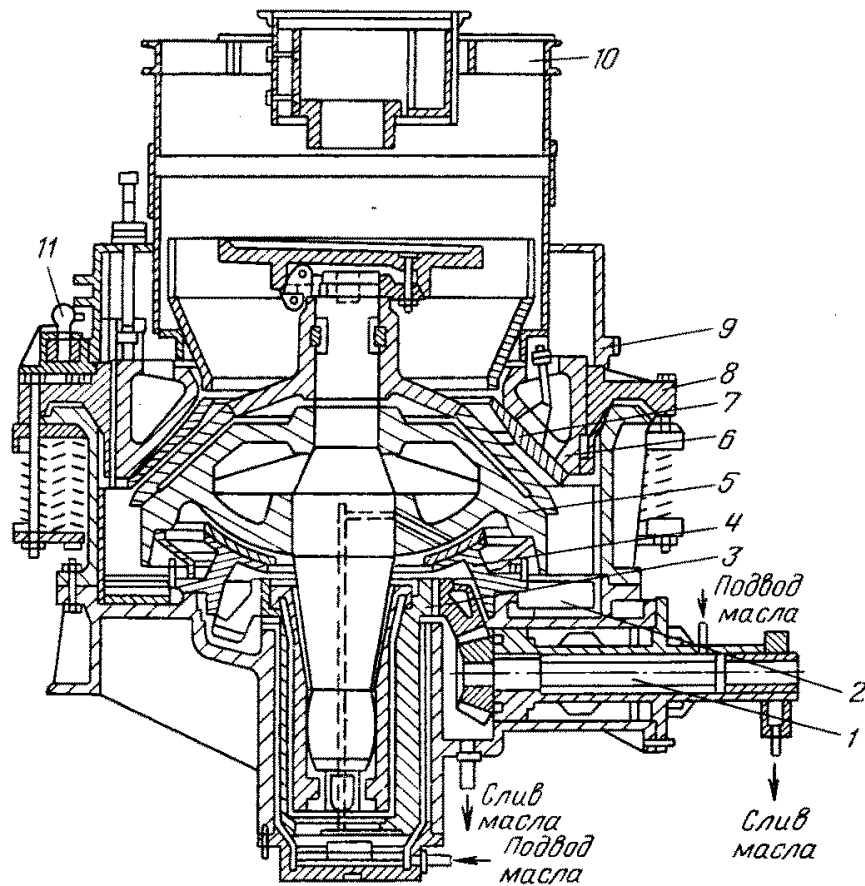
Принципова схема конусної дробарки дрібного дроблення:
